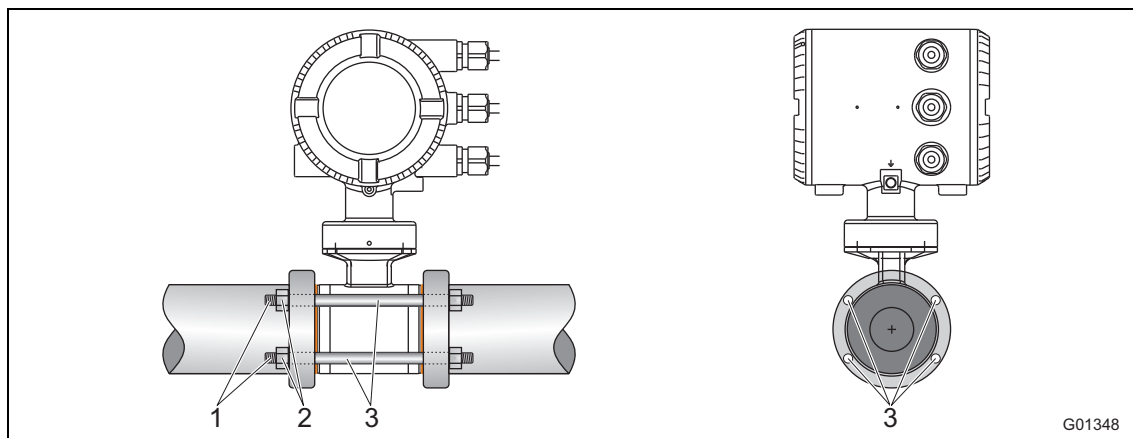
Set de montaje para dispositivos con diseño Wafer
